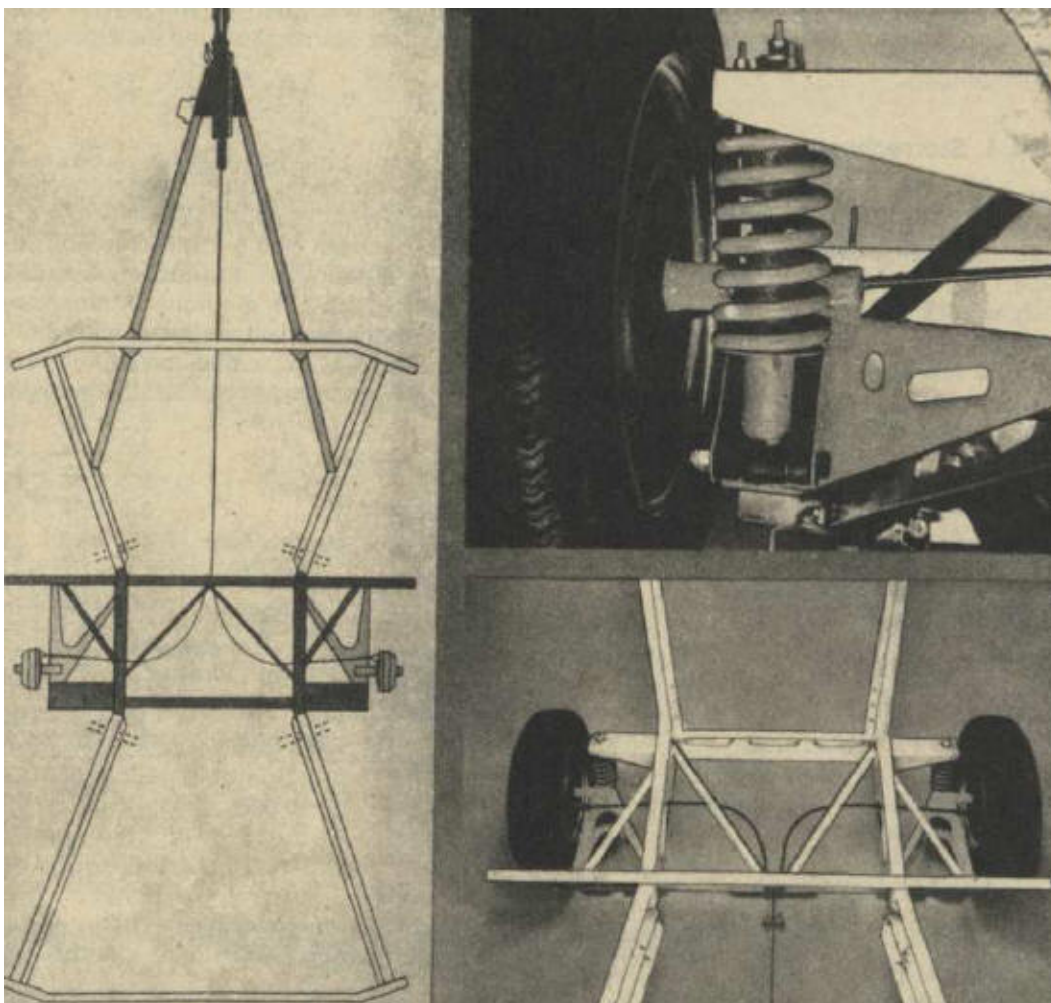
X-Chassis mit als Längslenker angebrachten Dreiecklenkern und Schraubenfederung [25]
